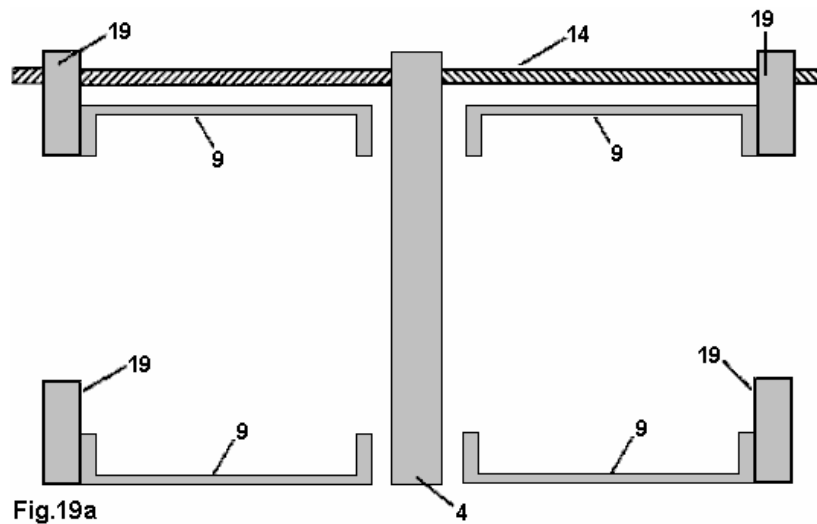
ziet u een longitudinale gedeelte door de mechanische behuizing voor het apparaat, dat wil zeggen een sectie parallel aan de as as 50. De mechanische behuizing omvat de steun stuk 4 voor de innerlijke stator 2 om te voorkomen dat het draaien, de mount 19 voor de begeleiding van de roerende helften van de buitenste stator 3, klemmen en een roterende threaded staaf 14 die beide helften van de buitenste stator 3 ten opzichte van de rotor en/of de innerlijke stator 2 kunt verplaatsen. De versnelling schacht 14 heeft twee schroefdraad secties met draden die in tegengestelde richtingen (links- en rechtsrijdend threads draaien). De rotatie van deze schacht zorgt ervoor dat de twee helften van de buitenste stator huisvesting als u wilt verplaatsen op symmetrische wijze in tegengestelde richtingen, naar binnen of naar buiten. De gids apparaten 19 zijn gemonteerd op de as versnelling 14 en dus ze alleen verplaatsen in één vlak. De buitenste cilindrische delen 9, die de buitenste stator 3 huis zijn stevig gekoppeld aan de eindkappen 19. Meestal heeft deze mechanische behuizing een hoogte van 400 tot 600 mm, een breedte van 400 mm en een diepte van 530 mm.
